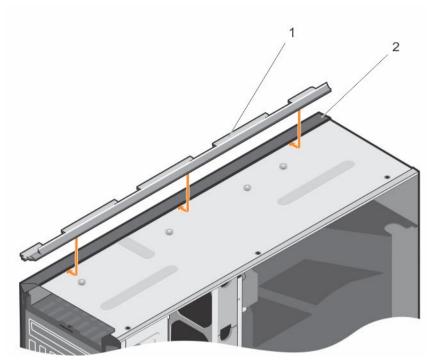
Extracción e instalación de la cubierta de deslizamiento del rack.
